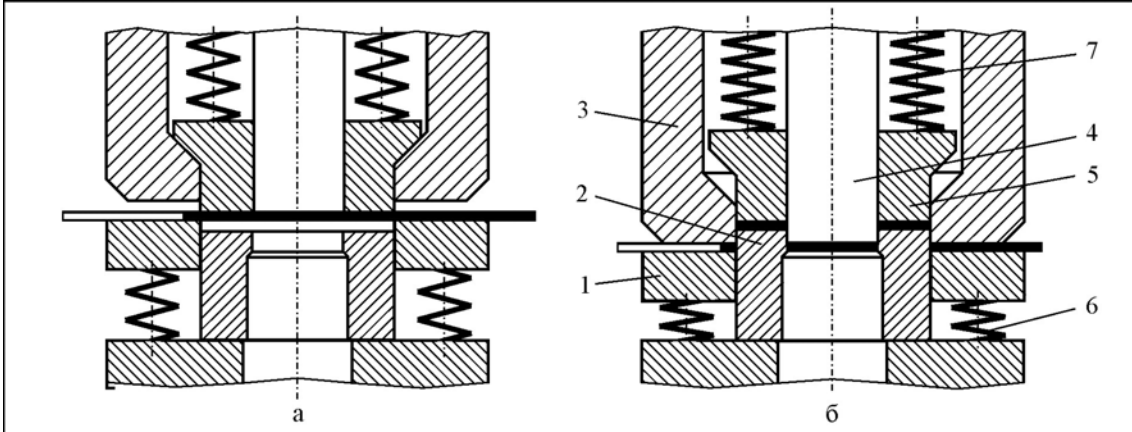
Схема робочої зони штампа суміщеної дії для штампування деталі «Шайба»: а – початкова фаза; б – кінцева фаза; 1 – нижній рухомий знімач; 2 – пуансон-матриця; 3 – вирубна матриця; 4 – пробивний пуансон; 5 – виштовхувач; 6, 7 – пружини стиснення
